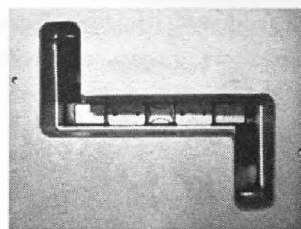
Verbundwerkzeug für den Einsatz von hochfesten Aluminiumlegierungen
